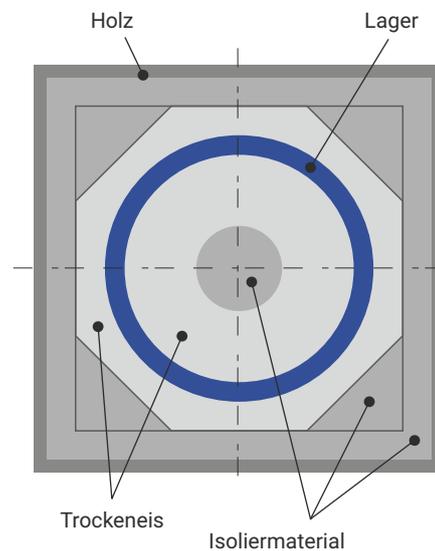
Holzbehälter für Trockeneis (Aufsicht)
